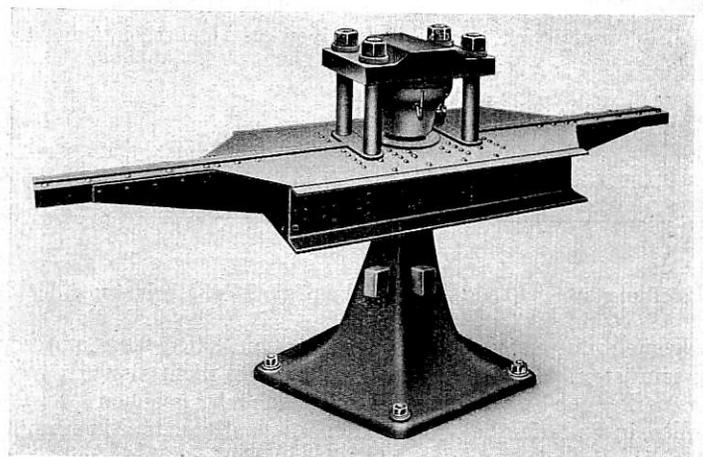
Auflagerung des Mittelteiles einer Windhoff-Drehzscheibe auf einem Kegelwalzenlager.
